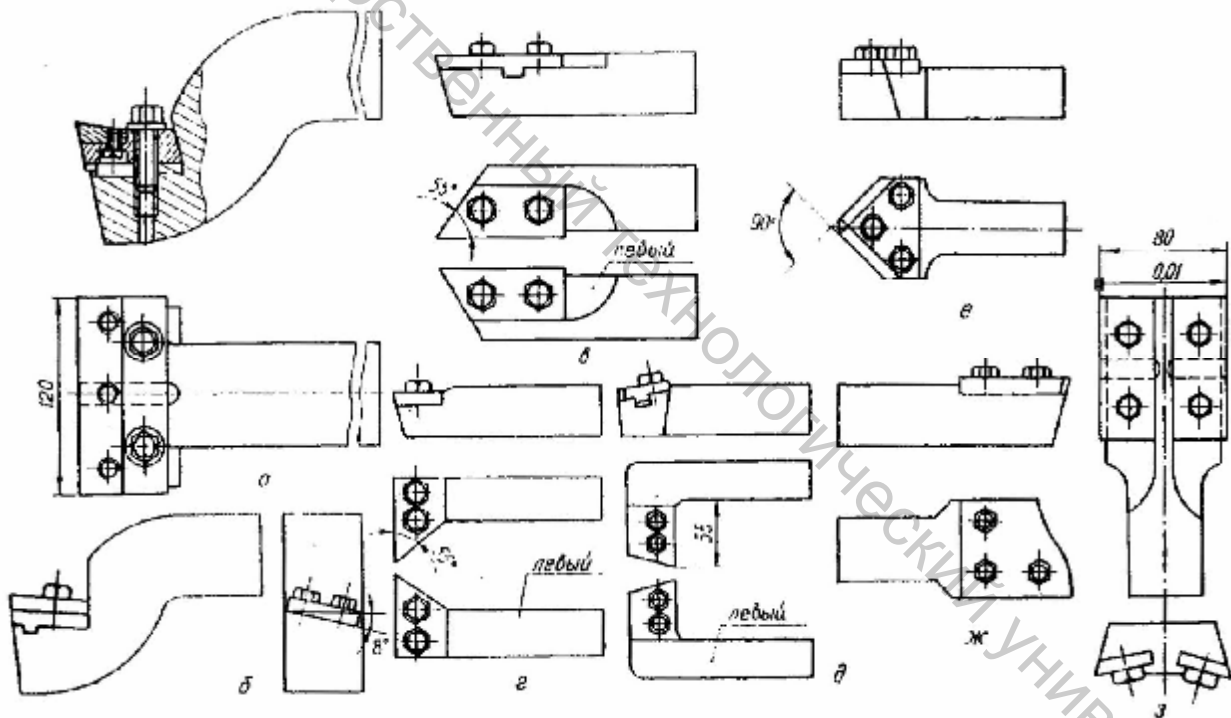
Строгальные чистовые резцы с механическим креплением режущих пластин из быстрорежущей стали:
